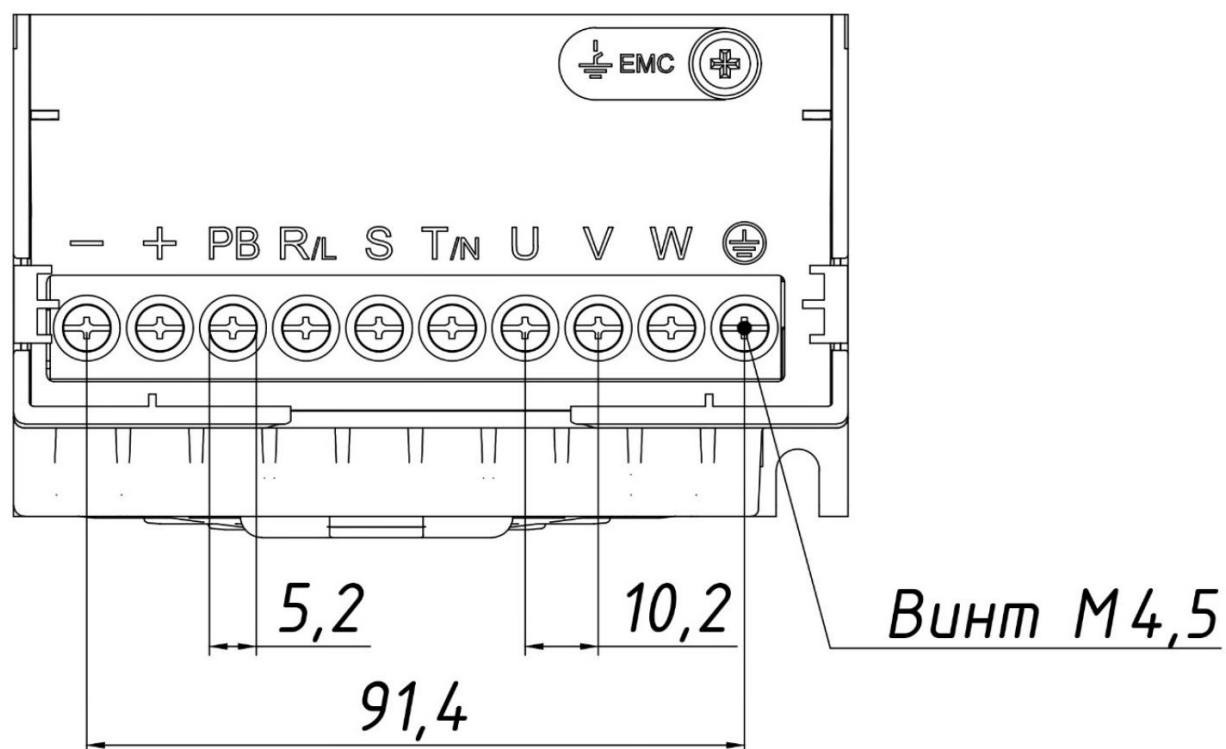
Размеры клемм цепи питания, типоразмер В3
